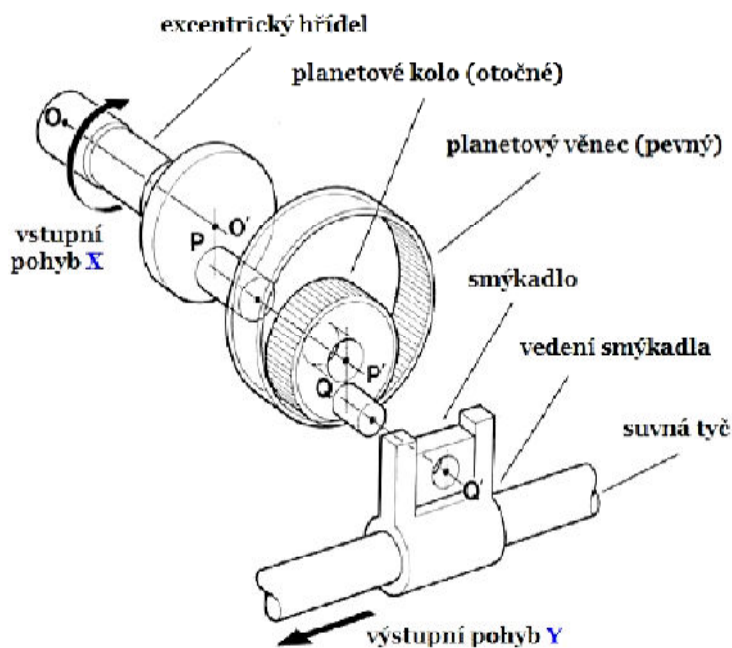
Konstrukce mechanické převodky řízení zadní nápravy [9]
